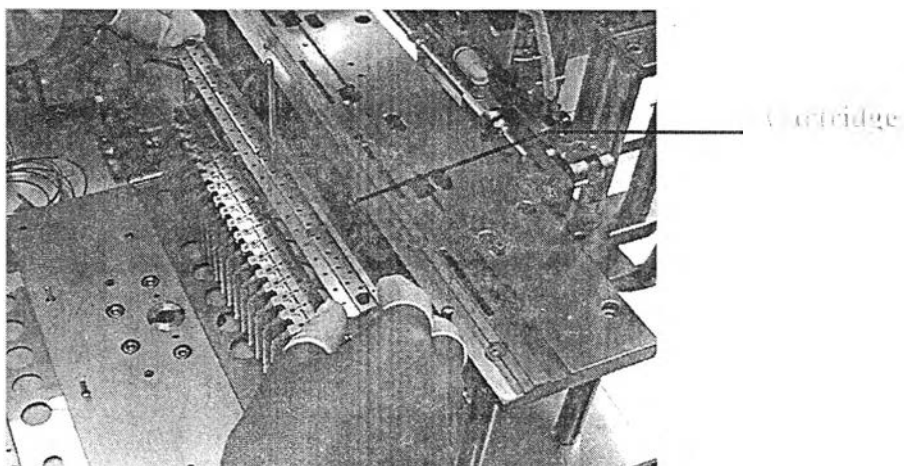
เครื่อง Laser welding machine
